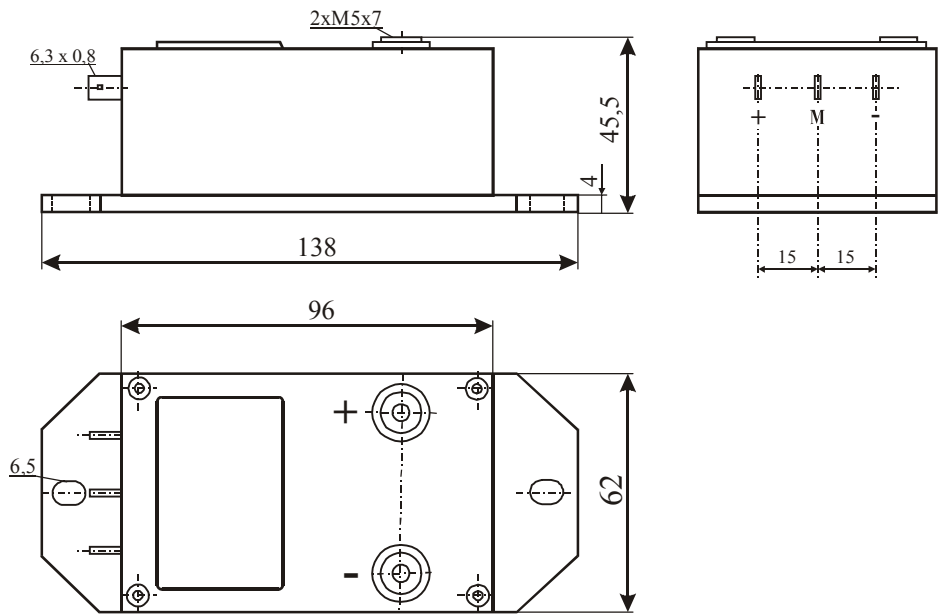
Внешний вид и габаритные размеры датчиков напряжения типа LV 100, LV 100/SP47
